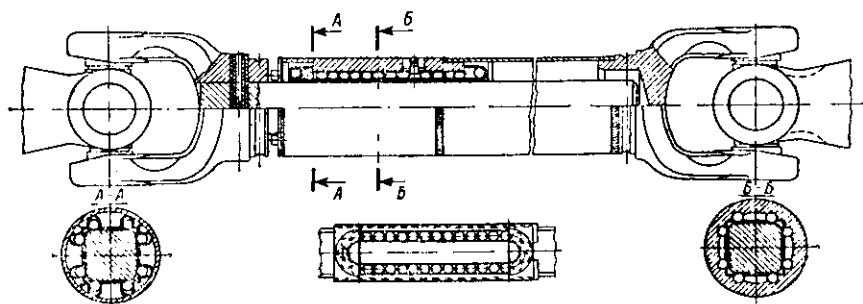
Карданный вал с шариковыми шлицами фирмы «Вальтершейд»
